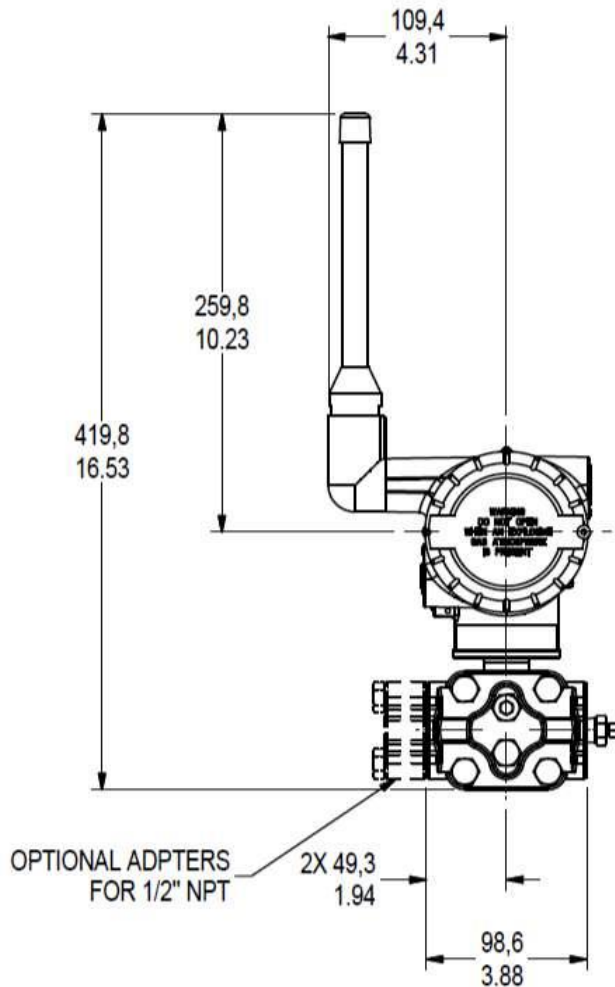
dimensions de montage types pour STDW810, STDW820, STDW830 et STDW870 (adaptateur d'antenne à distance illustré, vue arrière)
